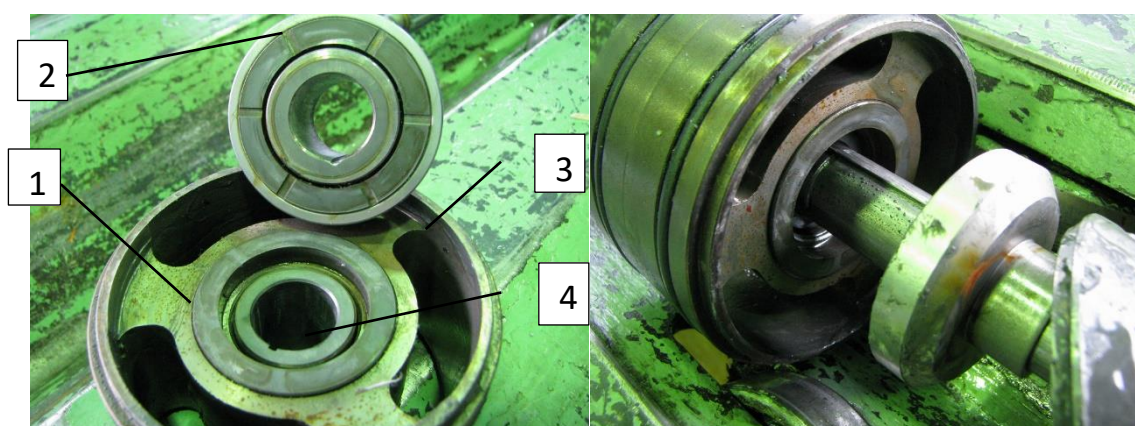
Общий вид радиально-упорного подшипников: 1-кольцо неподвижное, 2- кольцо вращающееся, 3-корпус подшипника, 4-штулка радиального подшипника
